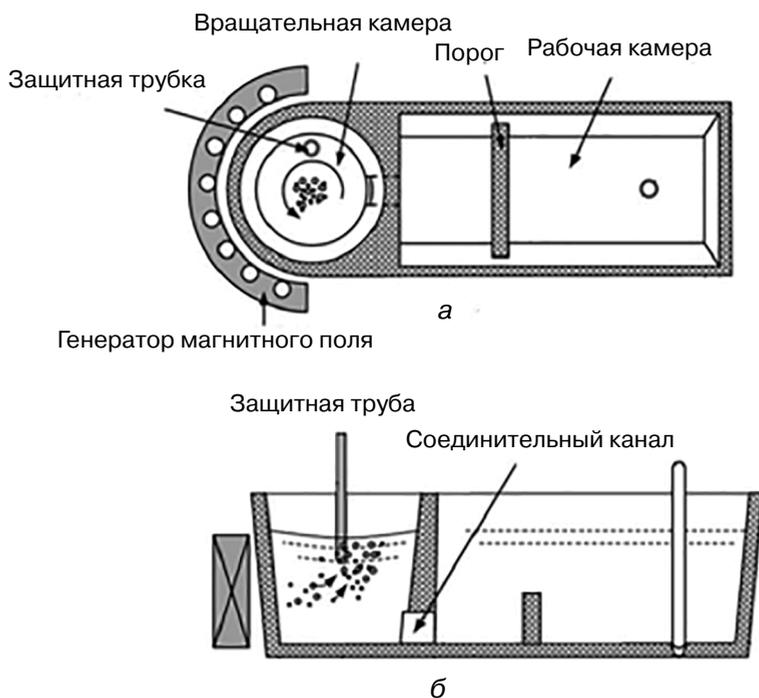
Двухкамерный промежуточный ковш с электромагнитным перемешивателем для создания вращающегося магнитного поля: а – вид сверху; б – фронтальная плоскость (сечение)
